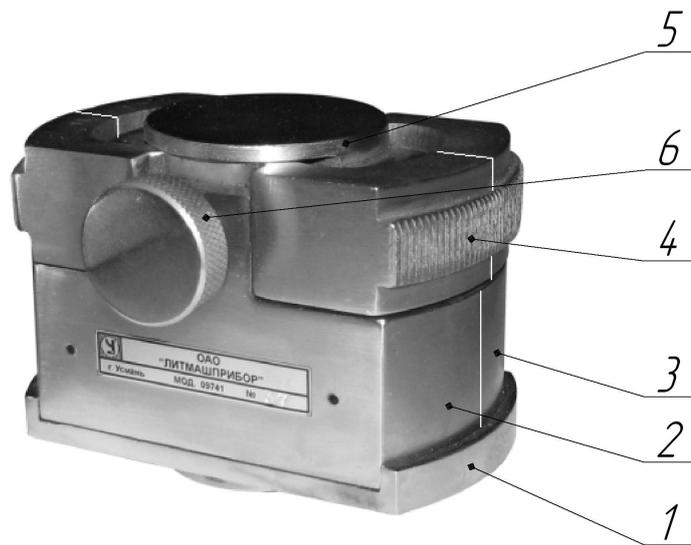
Стержневий ящик для виготовлення стандартних зразків (вісімок) для випробування на розтяг
